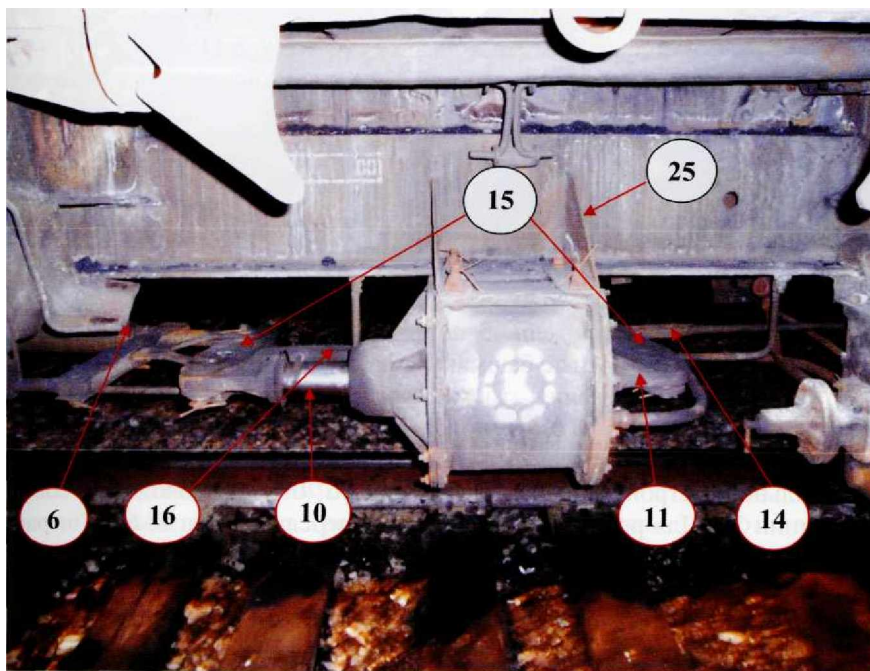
Конструкция тормозной рычажной передачи четырехосного грузового вагона (фрагмент 1)
